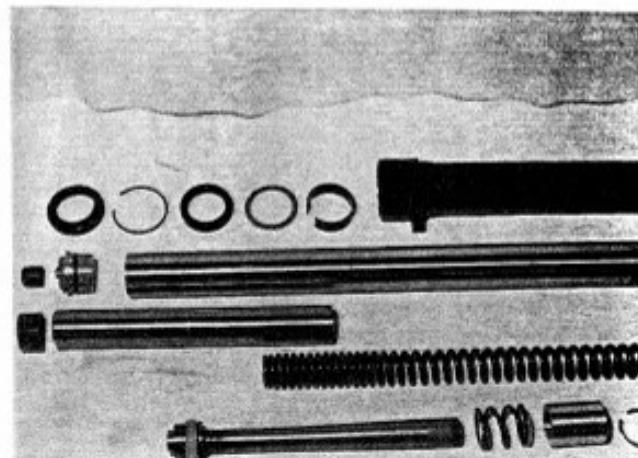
Wiedereinbau der rechten Gabelteile
